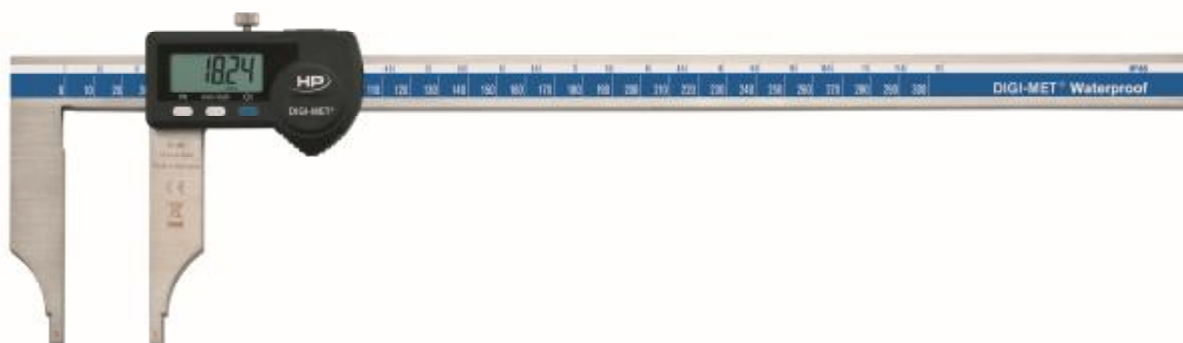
Общий вид штангенциркулей модификации 1242
